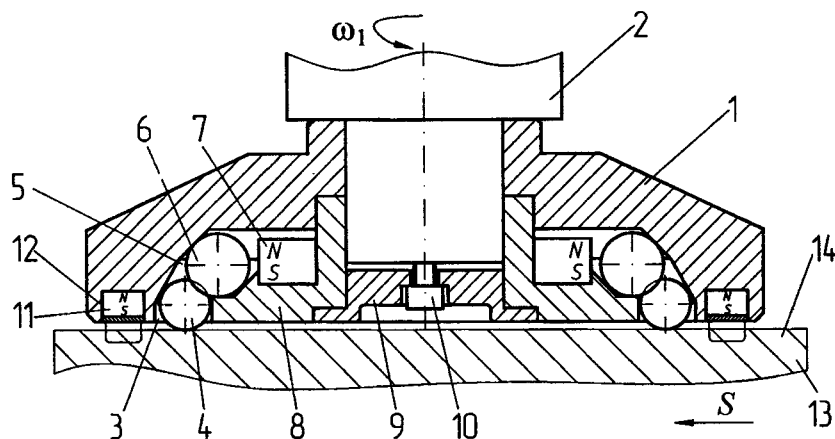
Инструмент для КМДН плоских поверхностей ферромагнитных деталей
